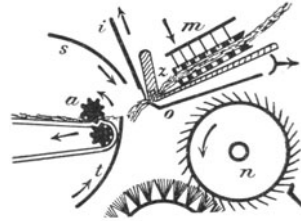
Wollkammer: Stellung der Werkzeuge beim Speisen.
